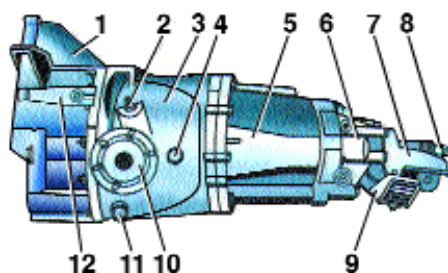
Коробка передач автомобилей «Святогор» (вид слева): 1 – картер сцепления; 2 – редуктор привода спидометра; 3 – картер главной передачи; 4 – маслозаливная пробка; 5 – картер коробки передач; 6 – крышка; 7 – кронштейн задней опоры двигателя; 8 – переключатель передач; 9 – задняя опора двигателя; 10 – фланец полуоси; 11 – маслозаливная пробка; 12 – рычаг выключения сцепления
